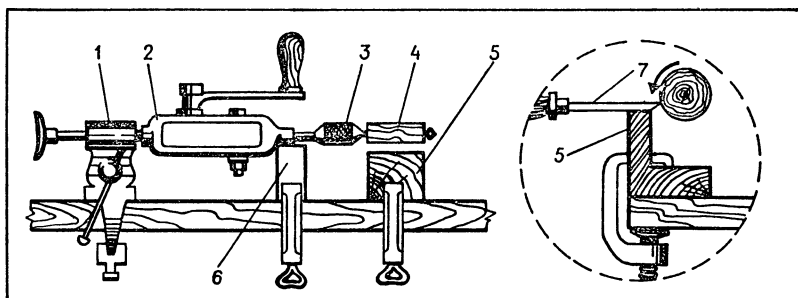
Использование дрели в качестве настольного токарного станка: 1 — тиски; 2 — дрель; 3 — патрон дрели; 4 — обрабатываемая деталь; 5 — подставка для стамески или напильника; 6 — подставка для дрели; 7 — стамеска.
